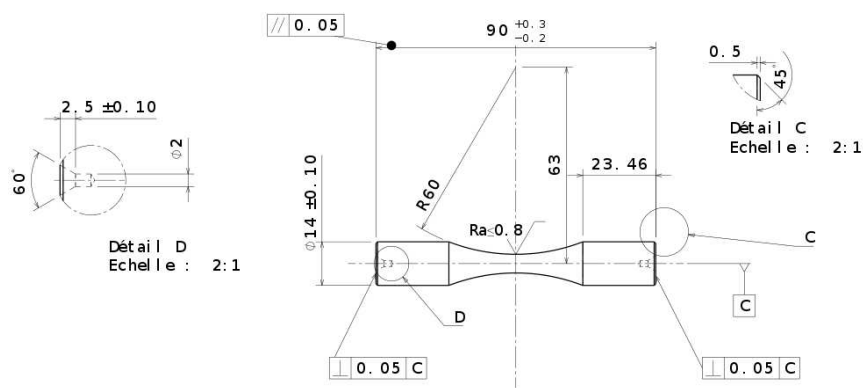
Géométrie des éprouvettes de fatigue en cuivre CuGF. L'axe longitudinal de l'éprouvette est parallèle à la direction d'étirage z (cf. figure 2.1)
